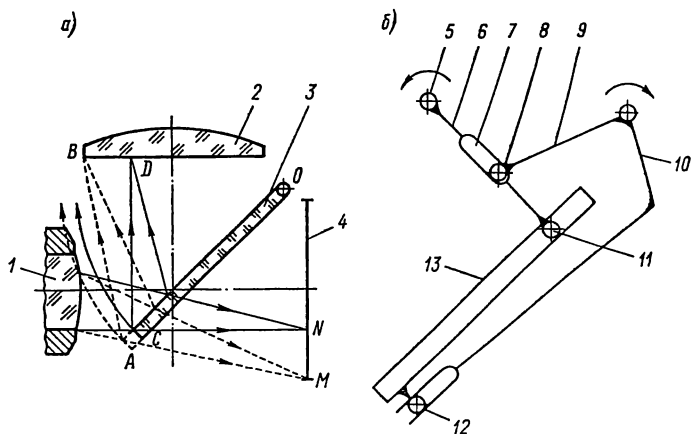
Поворотное зеркало: а — схема движения зеркала обычной длины; б — привод удлиненного зеркала
